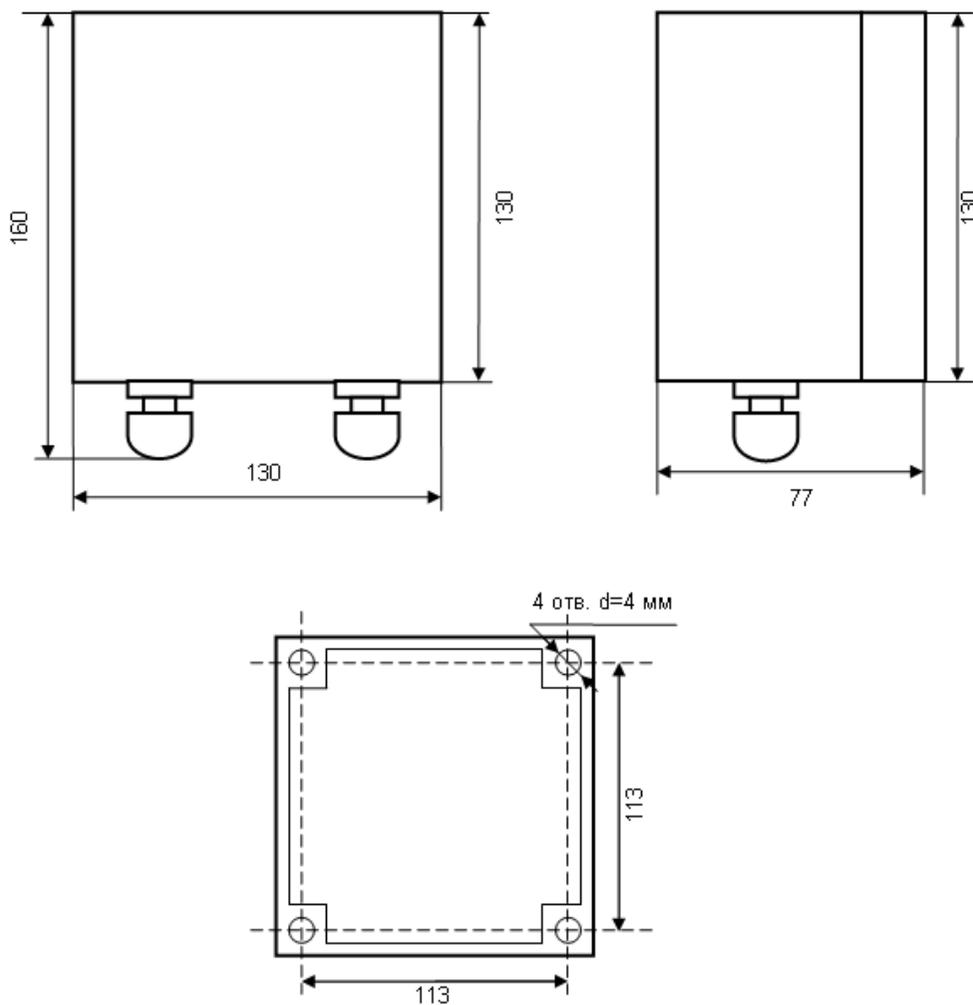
Габаритные и установочные размеры контроллера в герметичном исполнении.
